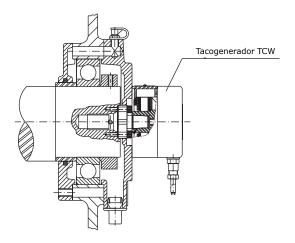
Conjunto acoplamiento tacogenerador TCW
